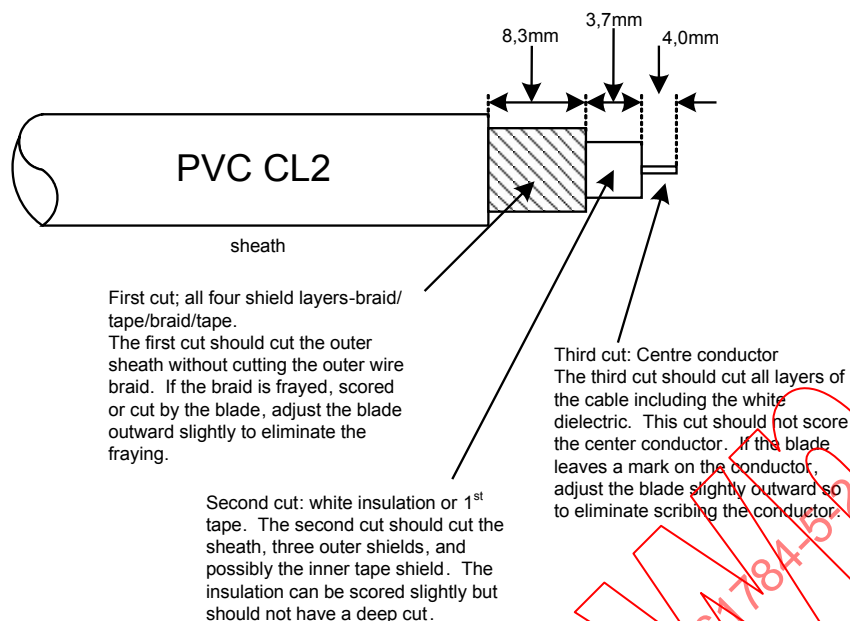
Étalonnage de l'outil de dénudage de câble coaxial
